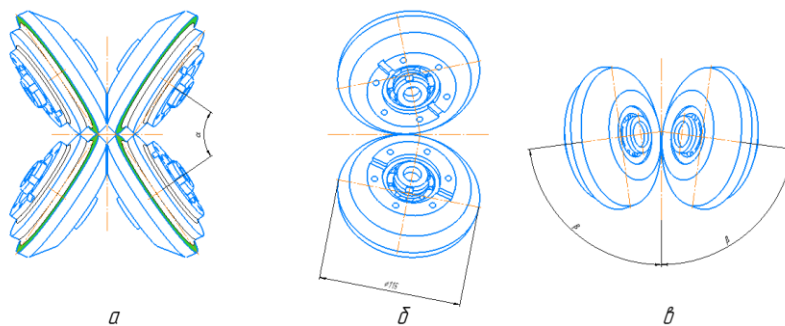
Загальний вид розташування прокатних валків для триниткової прокатки
